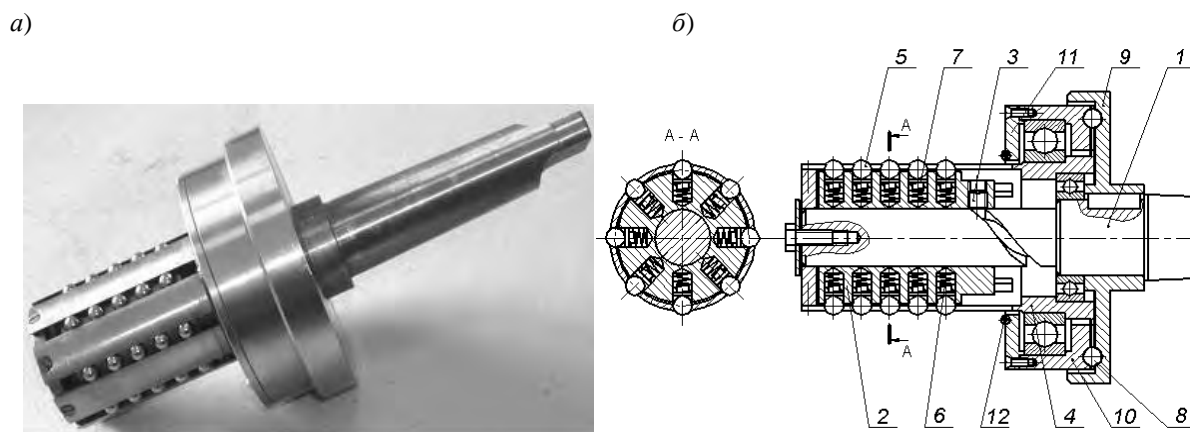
Инструмент для упрочняющей обработки выглаживанием внутренних поверхностей гидроцилиндров (а). Чертеж инструмента (б)
